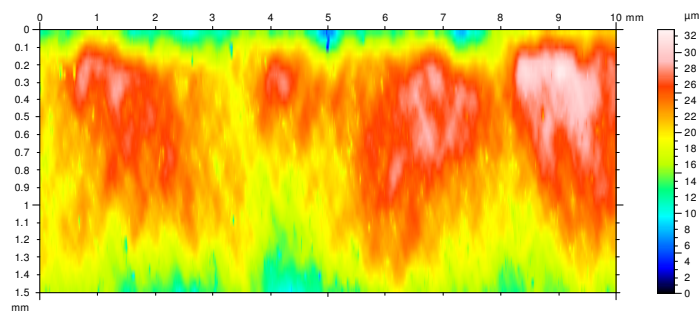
Wizualizacja foto 3D powierzchni obrobionej dla posuwu 56 mm/min i przy 355 obr/min
